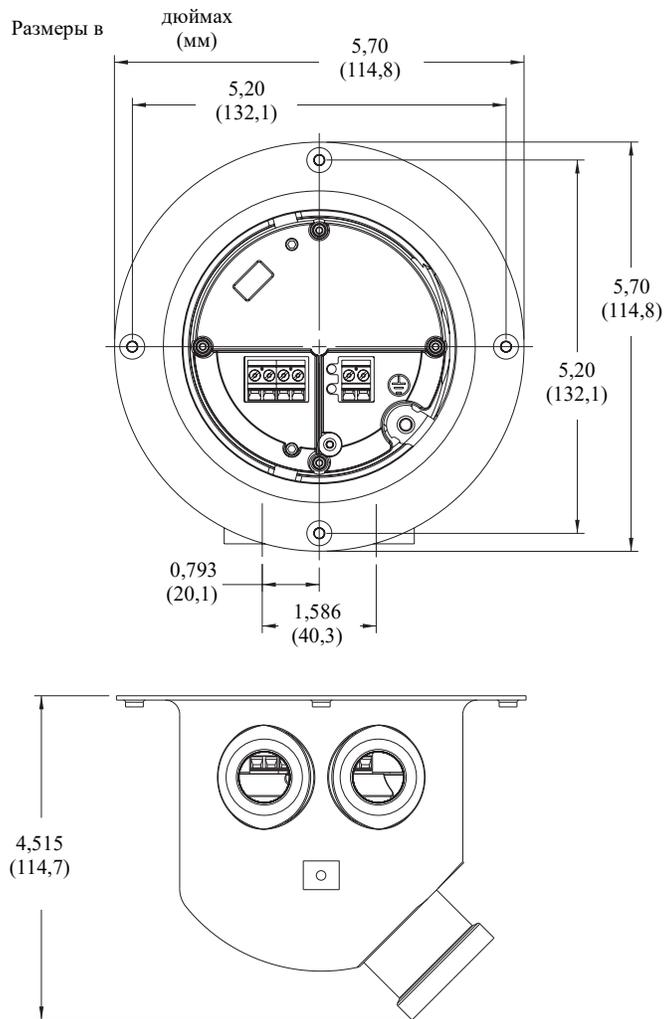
Размеры корпуса преобразователя для корпуса из нержавеющей стали
